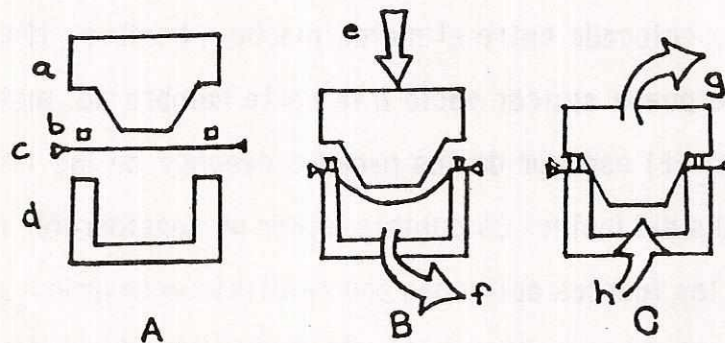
Formado por vacío y regreso instantáneo. A: Lámina precalentada previo al formado. B: Lámina estirada por medio de vacío, molde macho penetra la cavidad de la burbuja. C: Aplicación de vacío y presión para forzar la lámina en contra del molde macho: Molde macho con orificios de vacío. b: Anillo sujetador. c: Lámina precalentada y sujeta. d: Cajón de presión y vacío. e: Molde macho en movimiento. f: Vacío parcial para pre-estirar la lámina. g: Vacío. h: Presión de aire.
